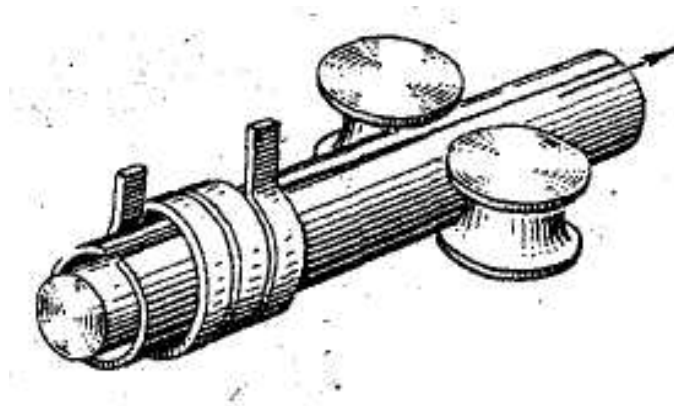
Схема високочастотного зварювання з індукційним підведенням струму
